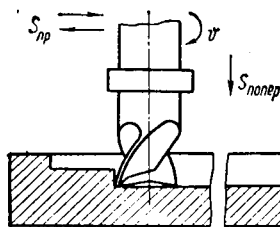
Фрезерование шпоночного паза в несколько проходов
